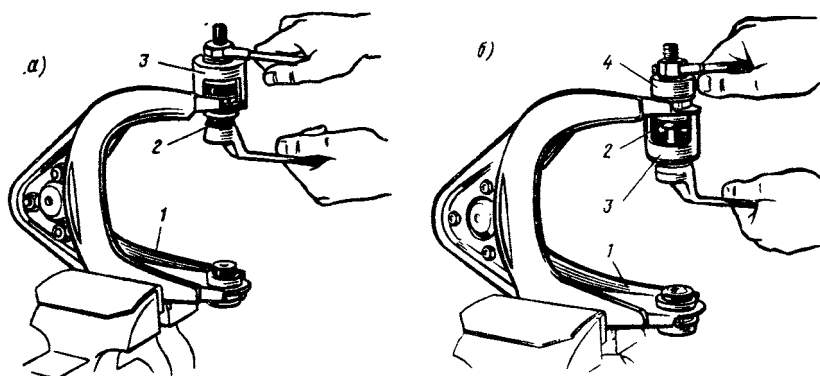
Замена резинометаллических шарниров верхнего рычага передней подвески: а — выпрессовка шарнира; б — запрессовка шарнира
